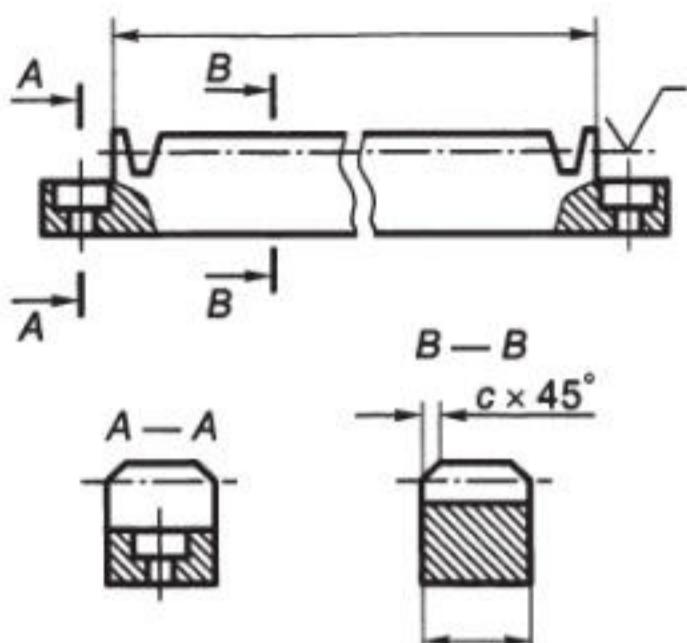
Пример указания параметров зубчатого венца на чертеже прямозубой зубчатой рейки со стандартным исходным контуром
